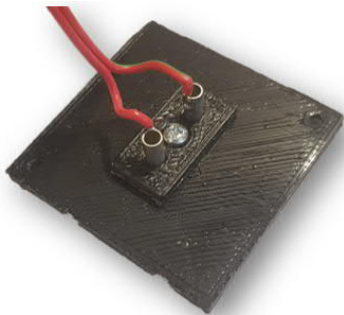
Befestigung der Kabel am Gehäusedeckel der Box
